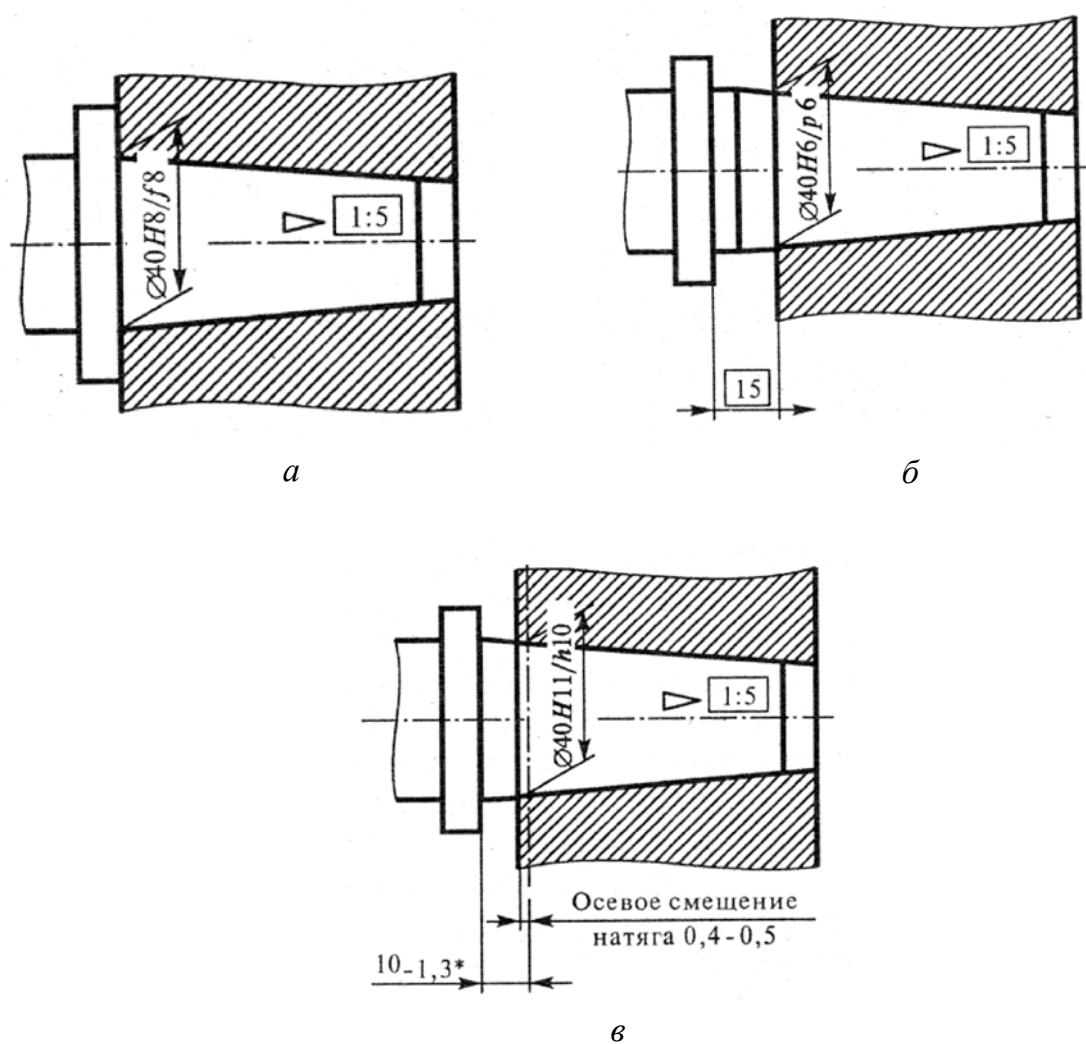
Обозначение гладких конических соединений на чертежах
